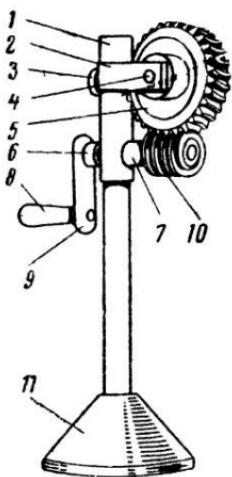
Модель червячной передачи: 1 — стойка; 2 — скоба; 3 — винт; 4 — ось; 5 — червячное колесо; 6 — упорное кольцо; 7 — вал привода; 8 — ручка; 9 — рычаг ручки; 10 — червяк; 11 — основание.
